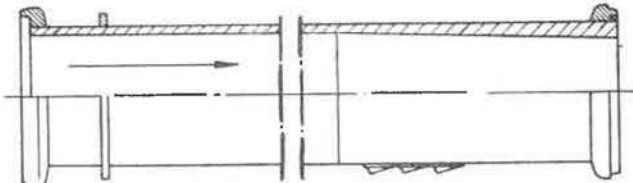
Tuyau de remblayage pneumatique de la firme Esser-Werke présentant à la sortie la forme d'une tuyère rétrécie.
